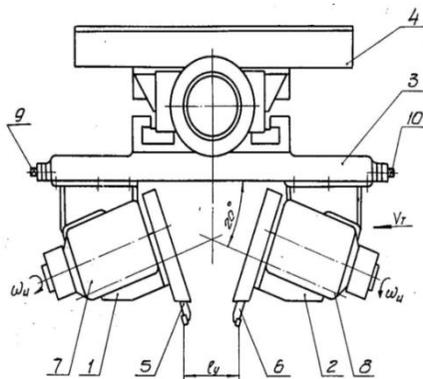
Принципиальная конструкция двухшпиндельного спецсуппорта к зубофрезерному станку мод. 5343
